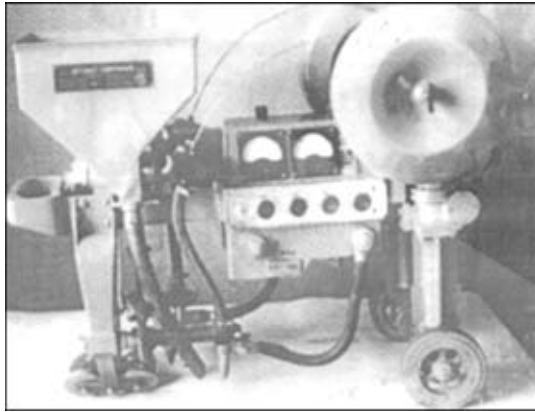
Автомат ДАСУ-138 для двухдуговой сварки под флюсом тавровых соединений одновременно с двух сторон
